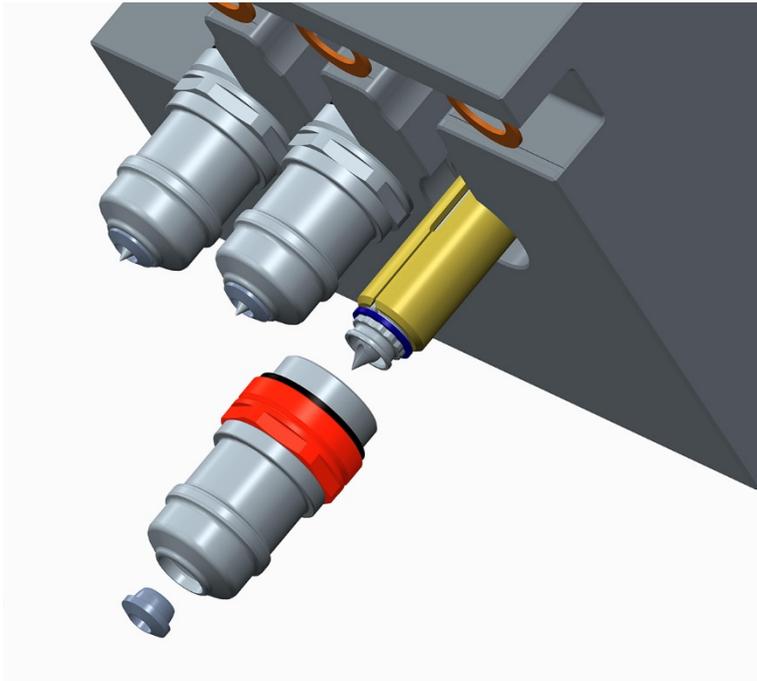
Detalle de la guía de montaje y desmontaje del casquillo (© Thermoplay)
